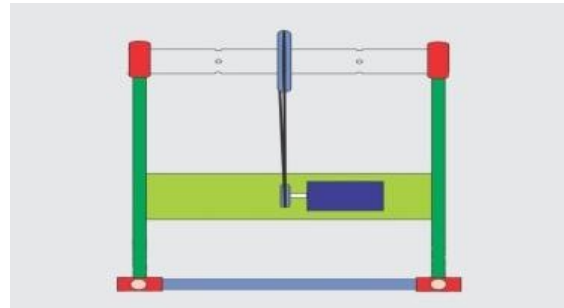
Konstruksi Alat Penabur Benih (tampak atas)
